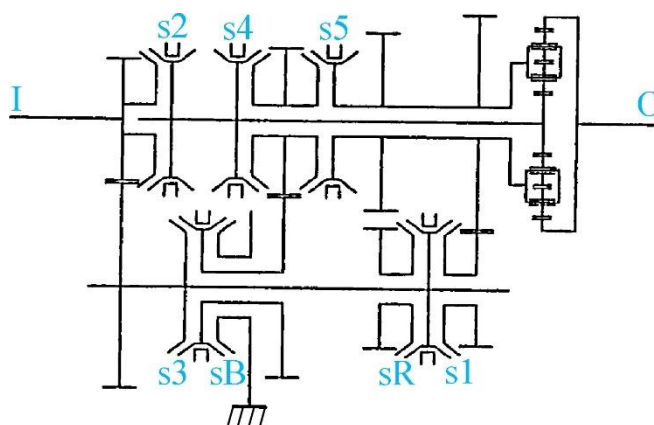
Кинематическая схема 8-ми ступенчатой вально-планетарной коробки передач.
